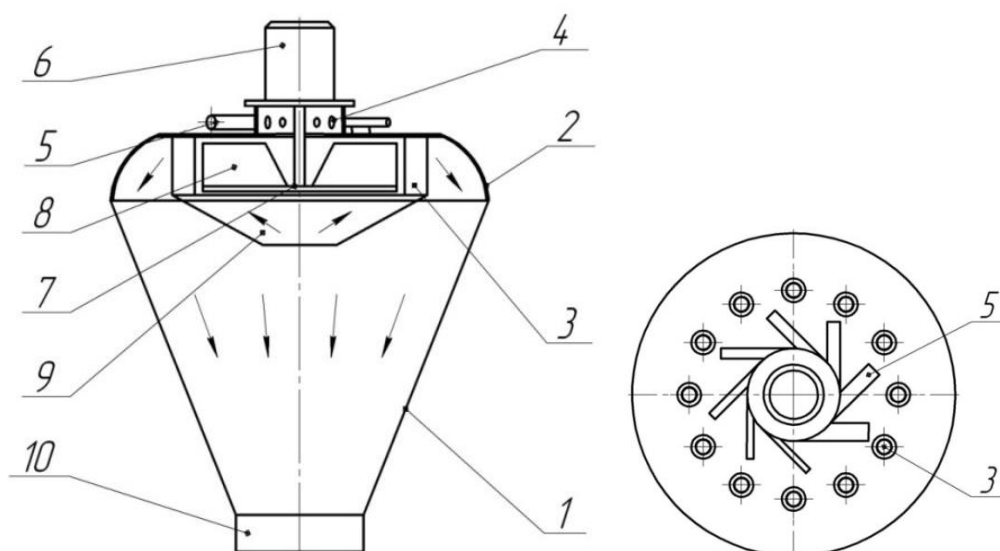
Аэродинамический смеситель сыпучих материалов: 1 – конический корпус; 2 – крышка; 3 – выходные патрубки; 4 – рабочая камера; 5 – всасывающие патрубки; 6 – электродвигатель; 7 – вентиляторное колесо; 8 – лопатки; 9 – конус; 10 – патрубок
